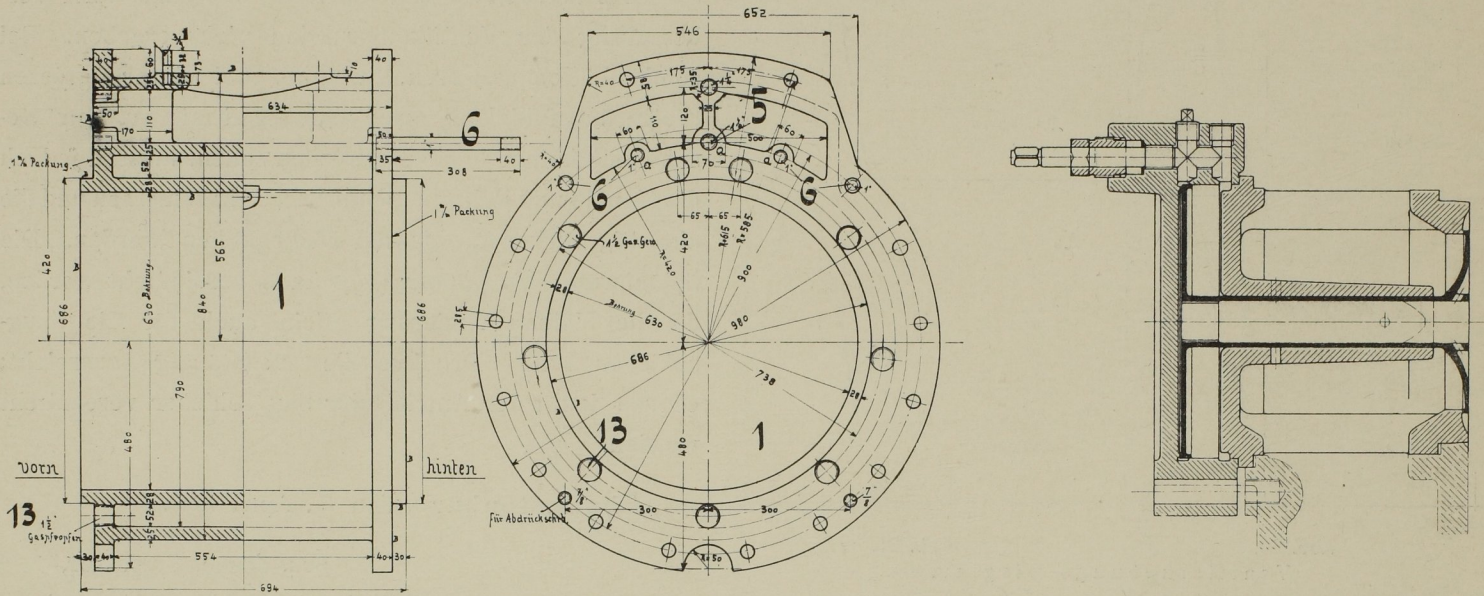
Kompressor-Cylinder. Masst. 1 : 15.
